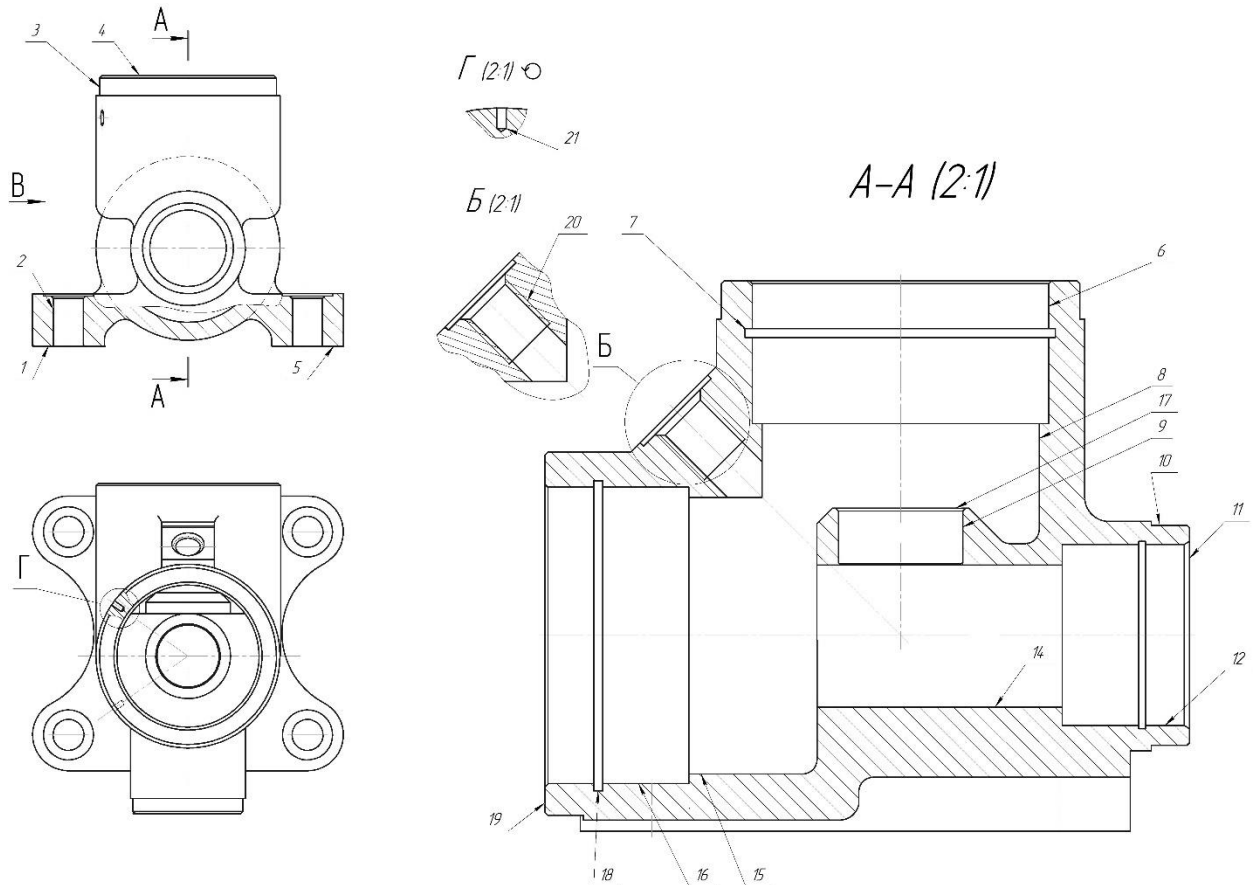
Ескіз деталі корпус УЯИШ.731347.006
